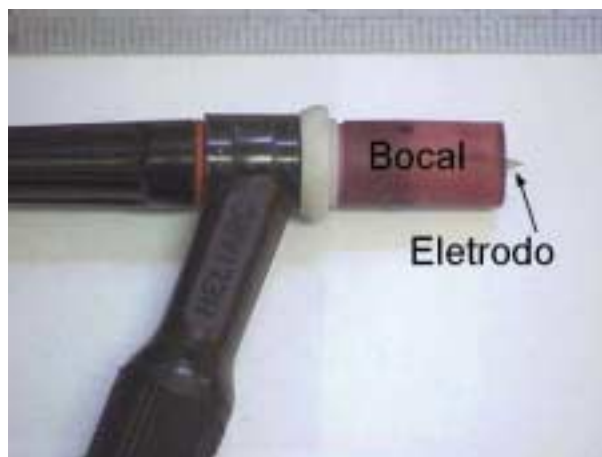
Detalhe de uma tocha para a soldagem GTAW
